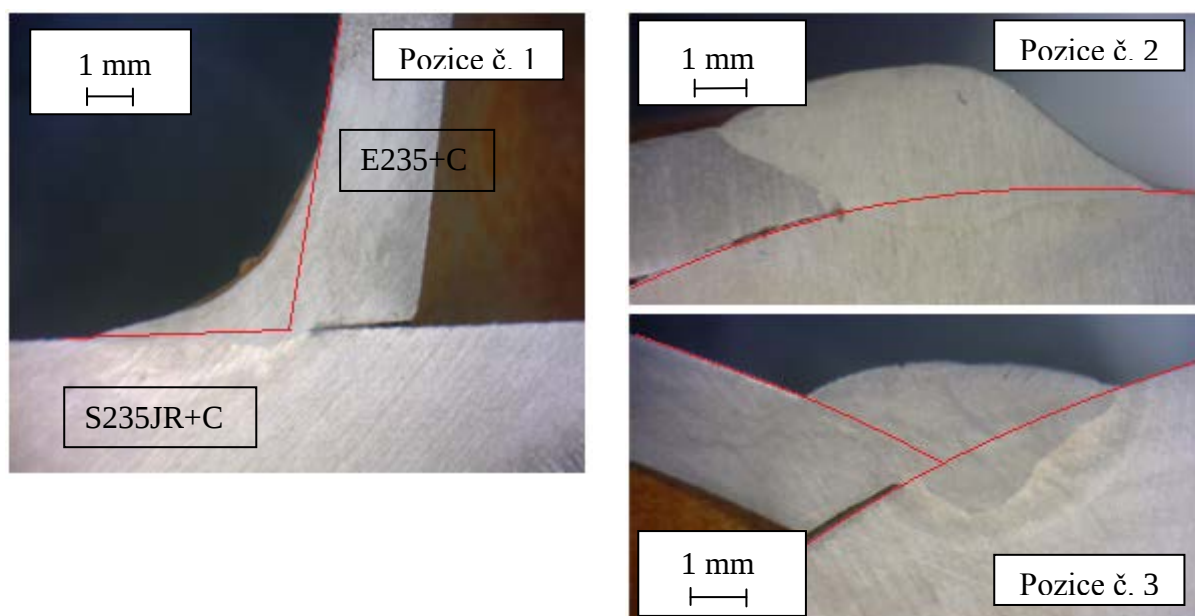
Makrostruktura svaru B10 vzorku č. 2
